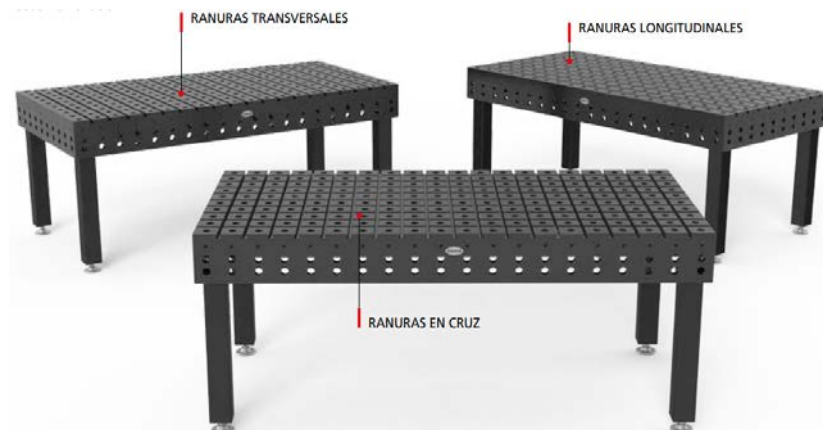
Mesa de soldadura ranurada (Siegmund)
